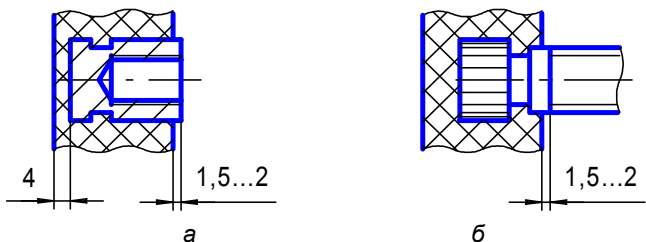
Рекомендуемые размеры установки в пресс-форме резьбовой втулки (а); стержня (б)
